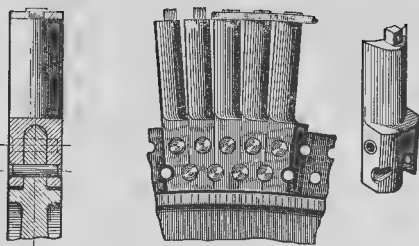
Лопатки с прикрепляемыми вилчатыми хвостами
